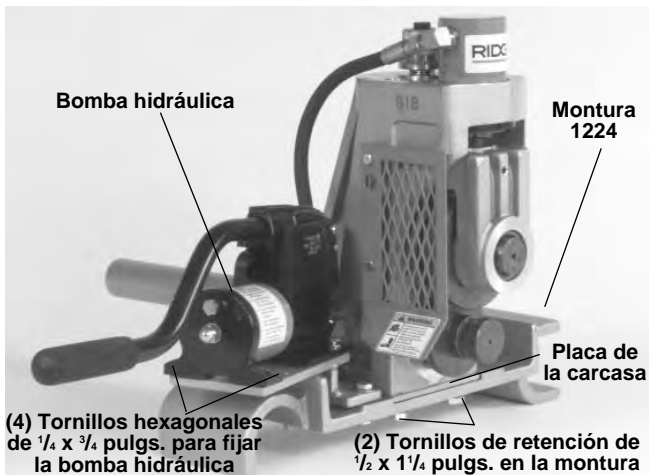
Ranuradora a Rodillos industrial No. 918 puesta sobre la montura de la Máquina Roscadora No. 1224
